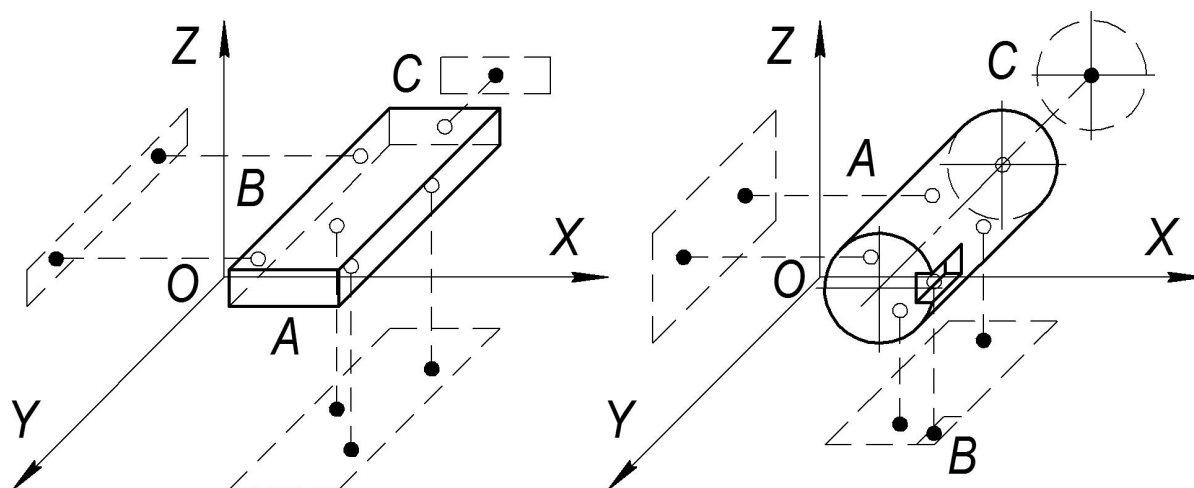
Схеми базування призматичної (а) і циліндричної (б) заготовок
